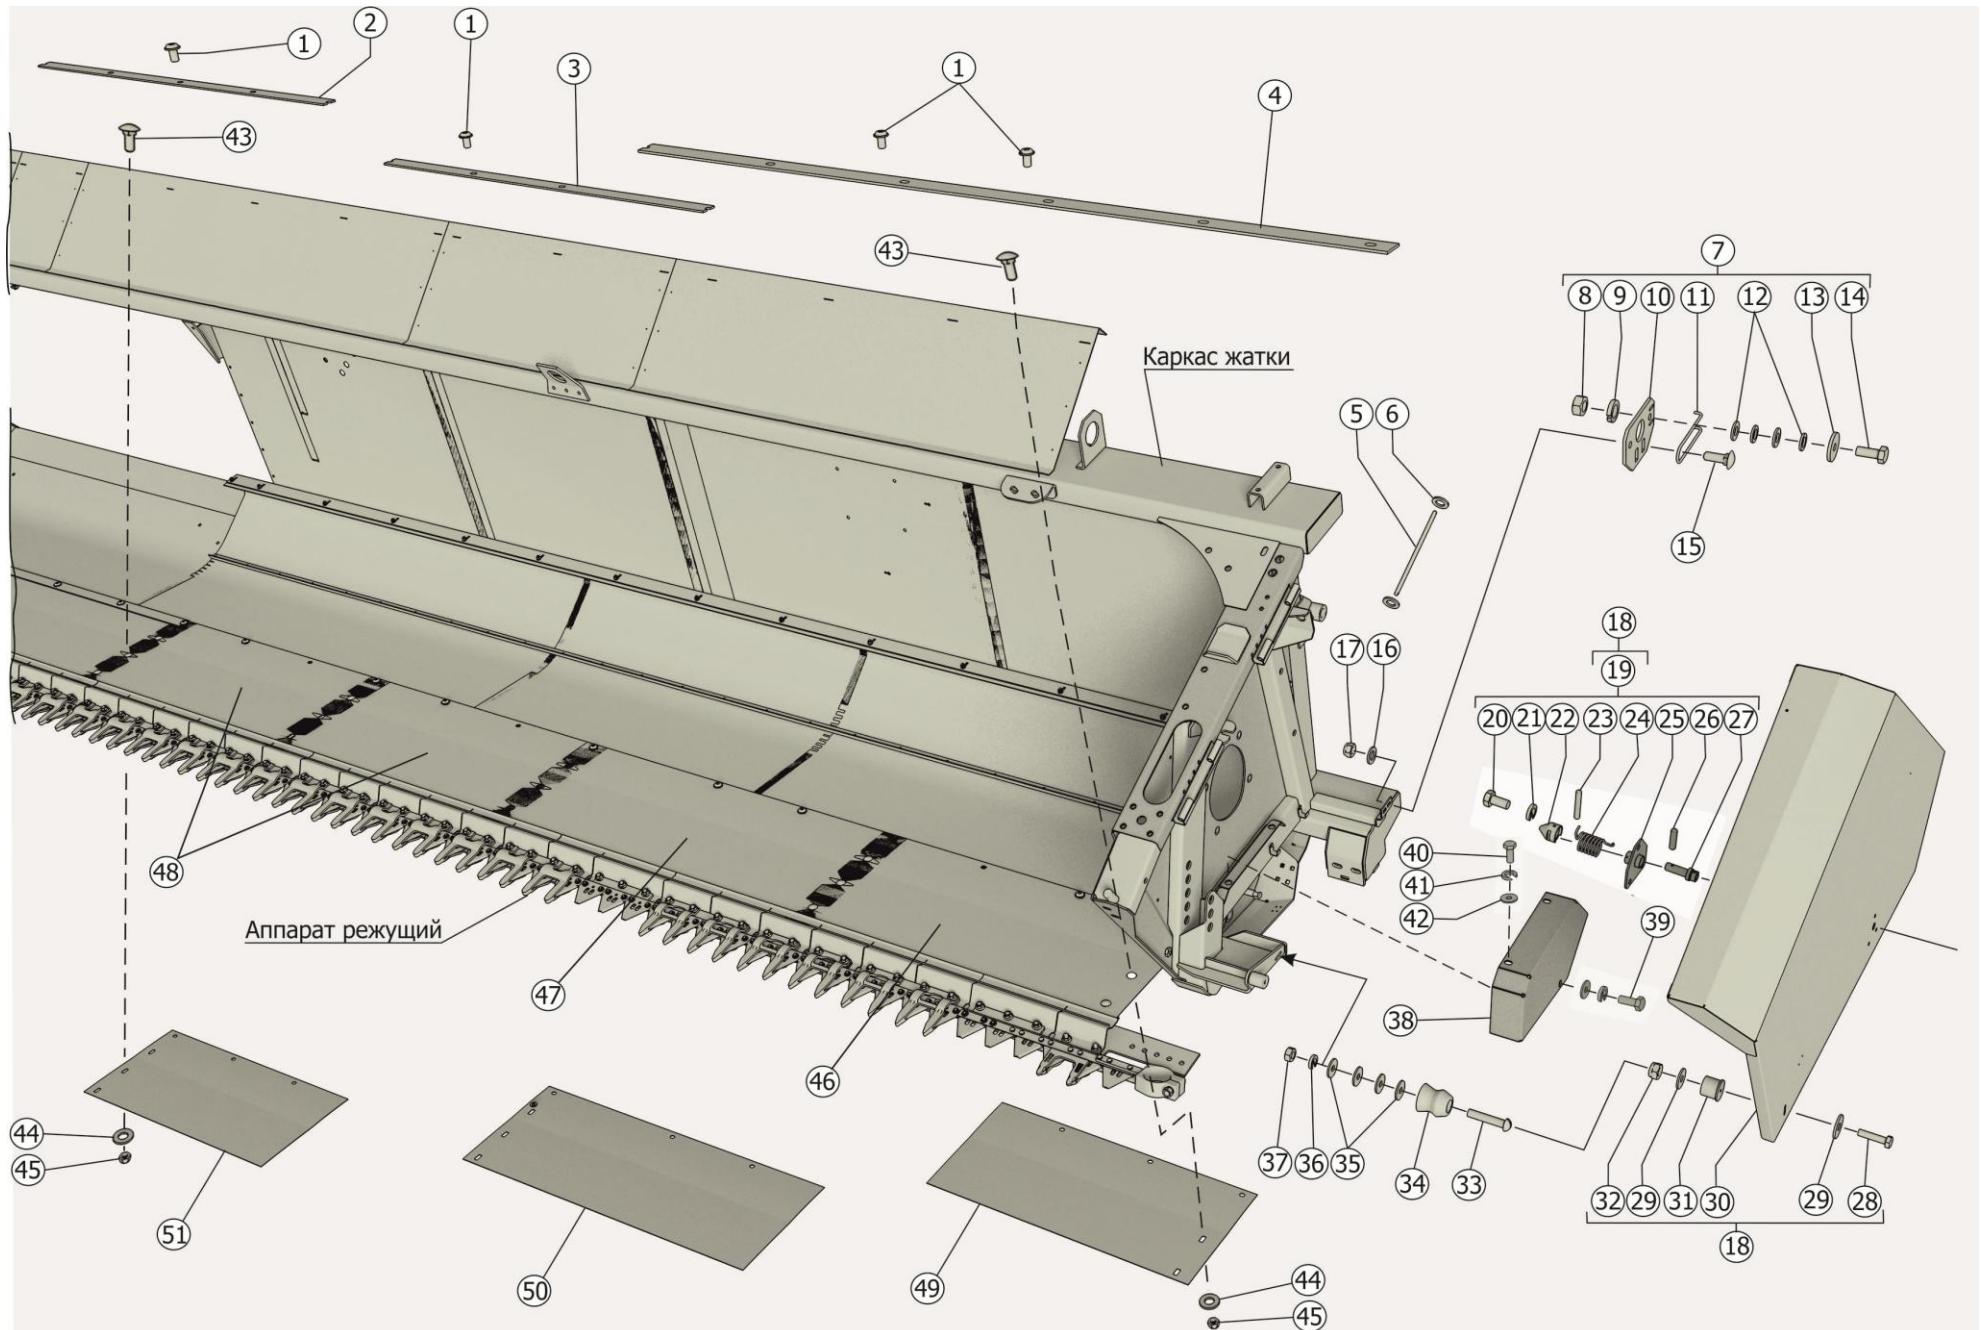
Установка щитов ЖСУ-901.11.00.000
